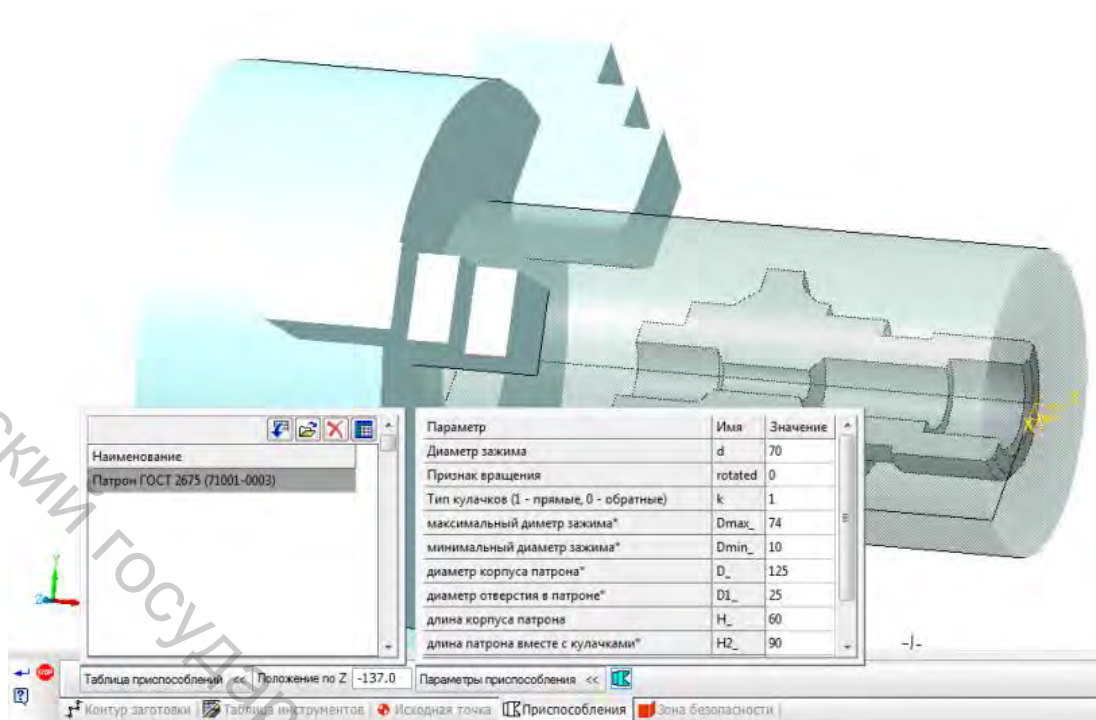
Выбор приспособления для зажима заготовки
